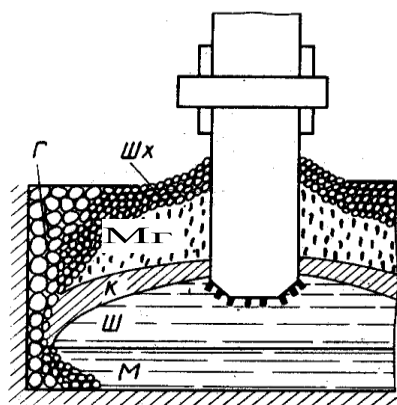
Ванна печи для выплавки углеродистого ферромарганца: М — металл; Ш — шлак; К — слой кокса; Мг — магма; Шх — шихта; Г — гарниссаж
